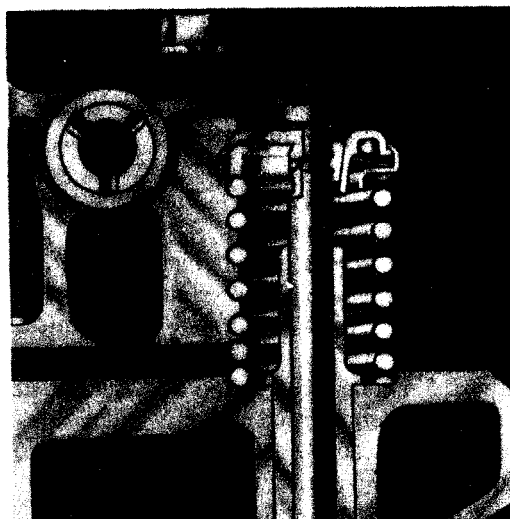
Instalación de un rotador forzado en un motor de válvulas en cabeza (TRW Inc.).
